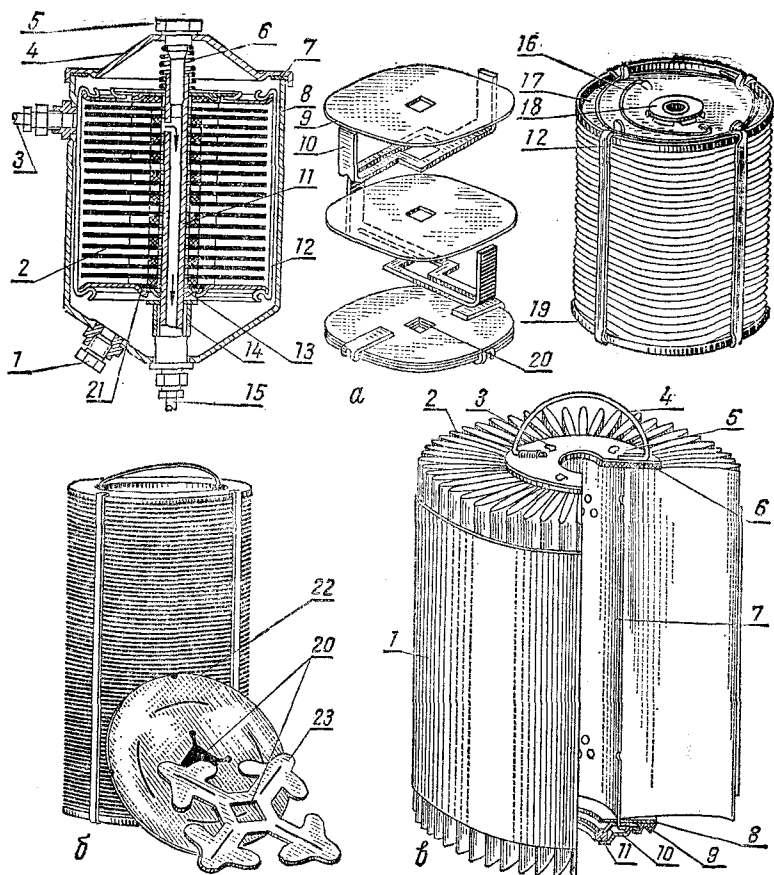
Фильтр тонкой очистки масла двигателей ГАЗ-21А и ГАЗ-52-01 и сменные фильтрующие элементы:
